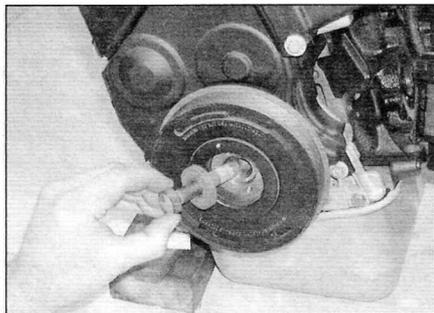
Выверните болт, снимите его вместе с шайбой и снимите шкив коленчатого вала (двигатели 2.0 л)
